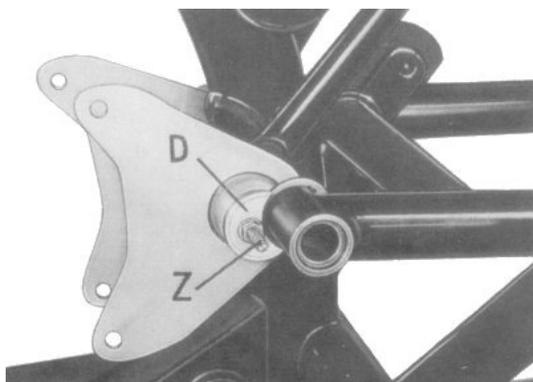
Motorbefestigungsbleche durch Druckring (D) und Zugspindel (Z) M 6 axial zusammengedrückt, Hinterradschwinge aufgeschoben
